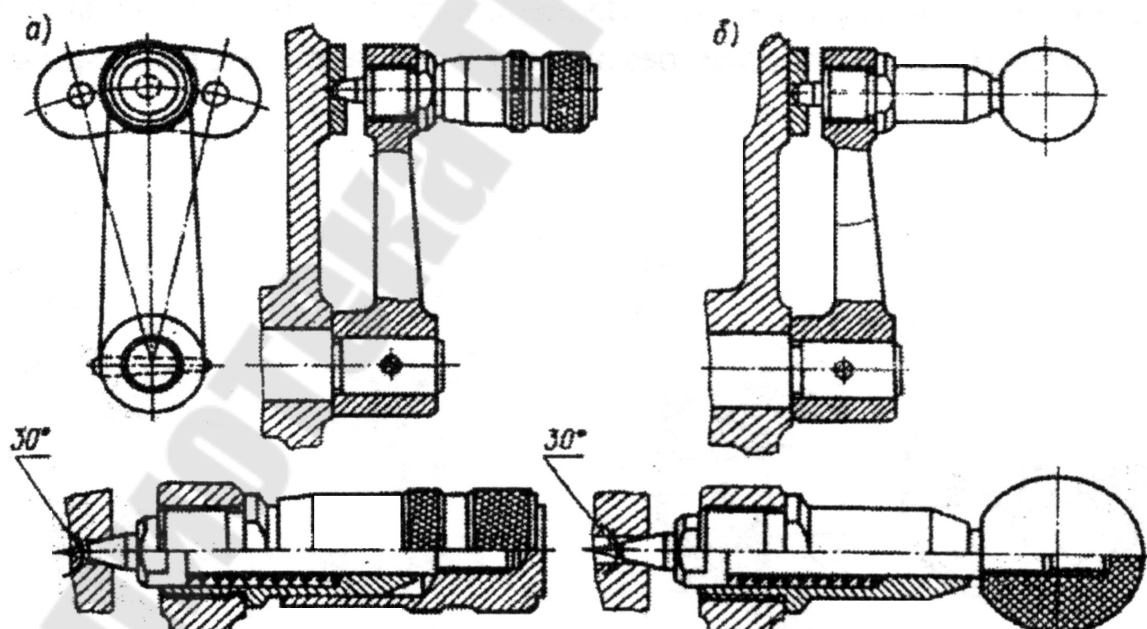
Конструкции рукояток с вытяжным фиксатором
